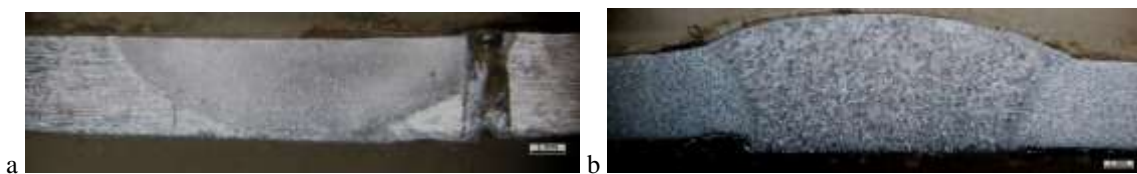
Macrografías de AA1050 soldado por: a-FSW, b- GMAW.
